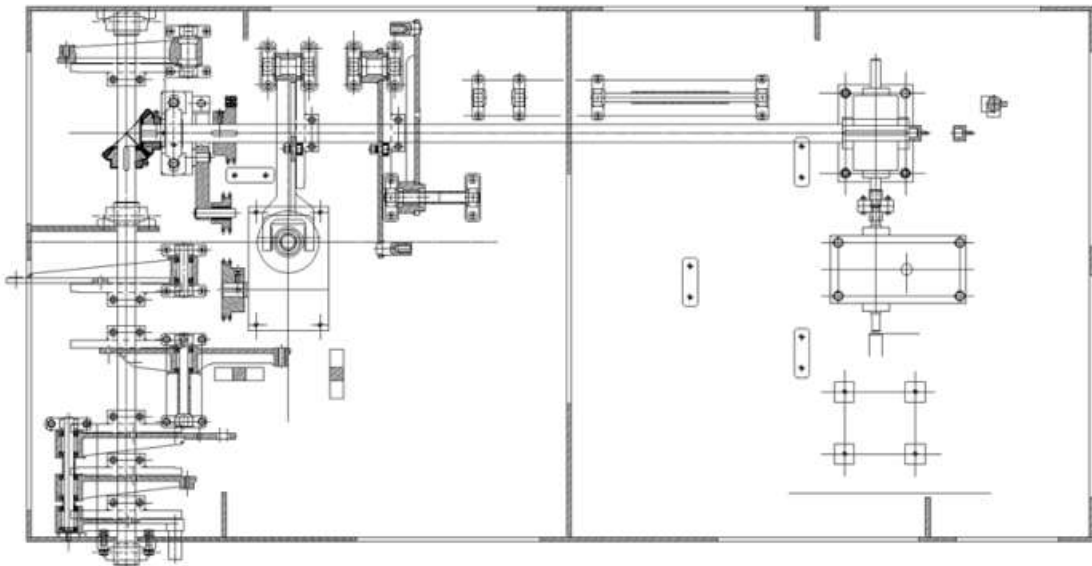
Auto Packaging M/C 구동부의 2D 설계도면
